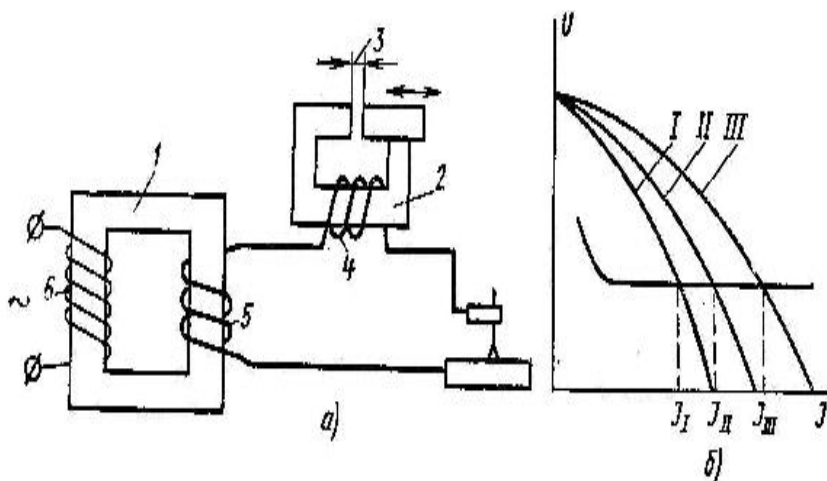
Схема сварочного трансформатора с последовательно включенным дросселем
